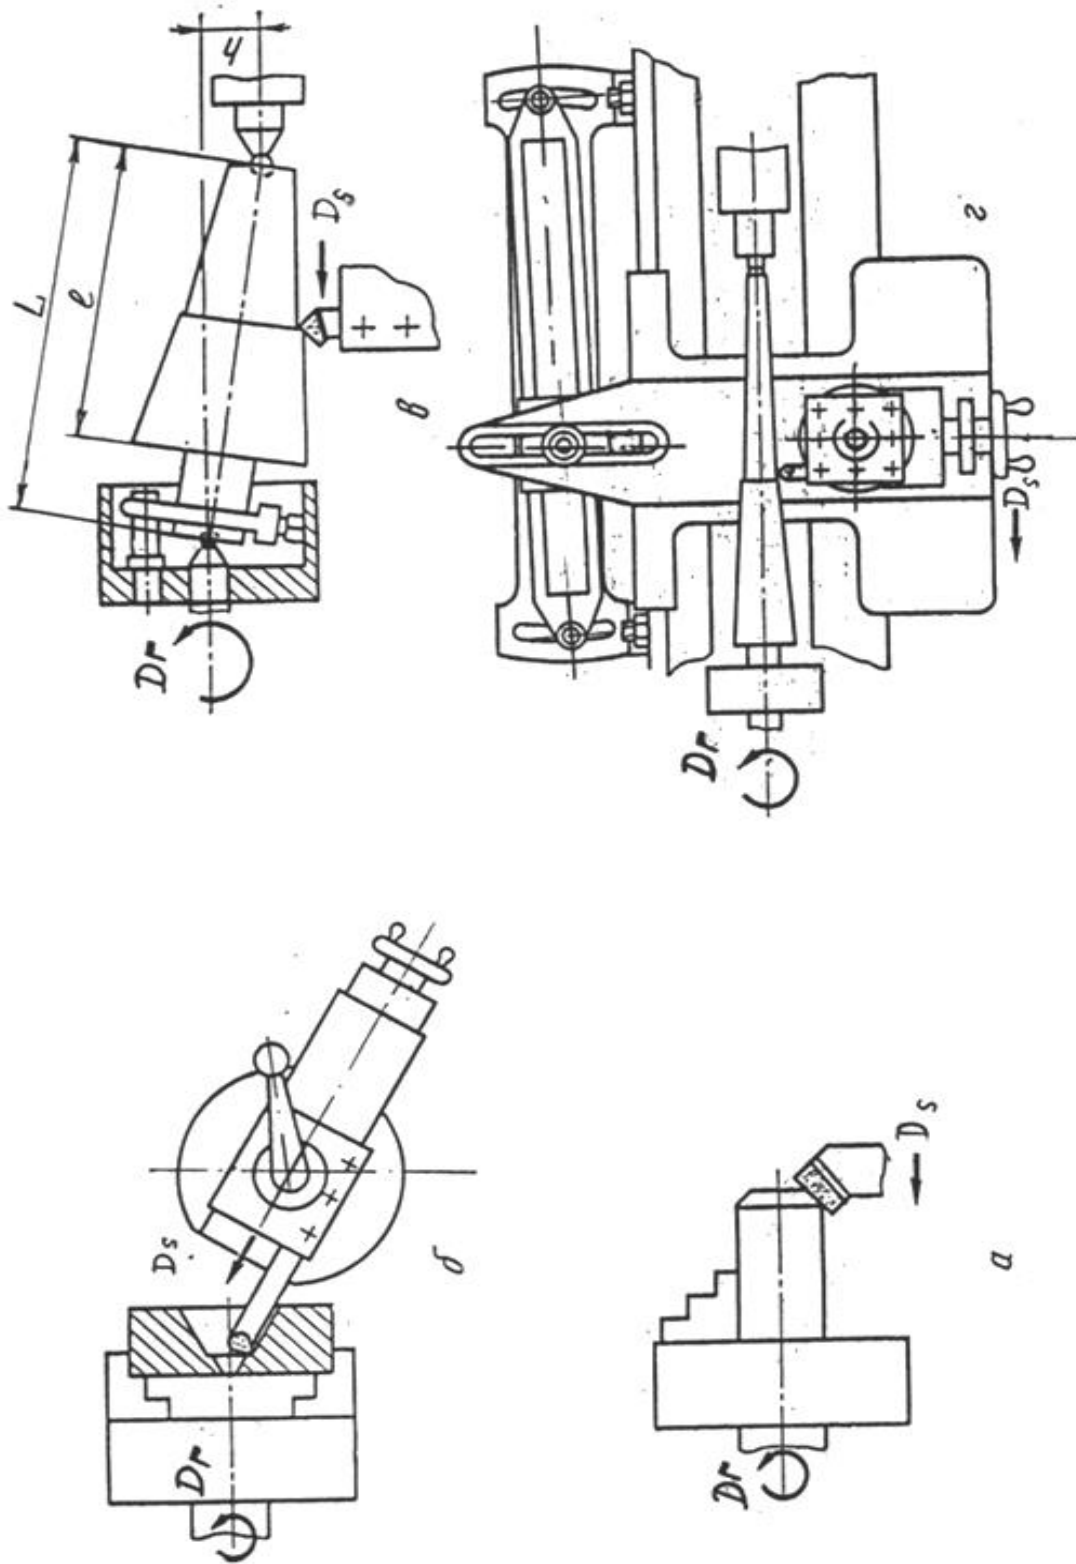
Способы точения конусов: а - широким резцом; б - поворотом верхней части суппорта-салазок; в - поперечным смещением центра задней бабки; г - с копировальной линейкой.
